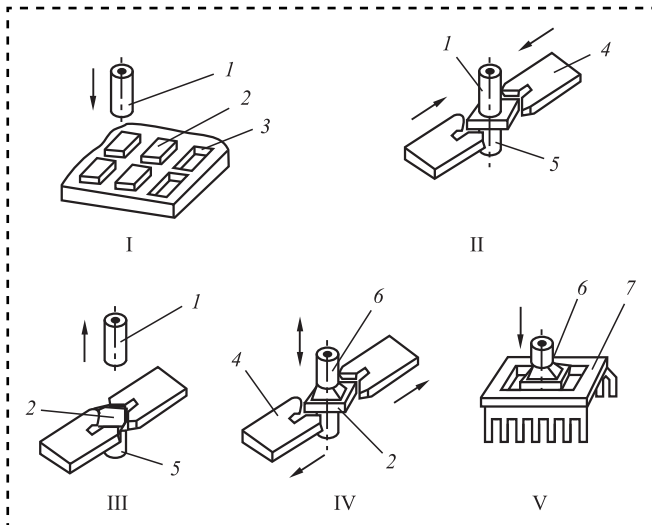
Основные этапы рабочего цикла установки кристалла в корпус ИМС:
